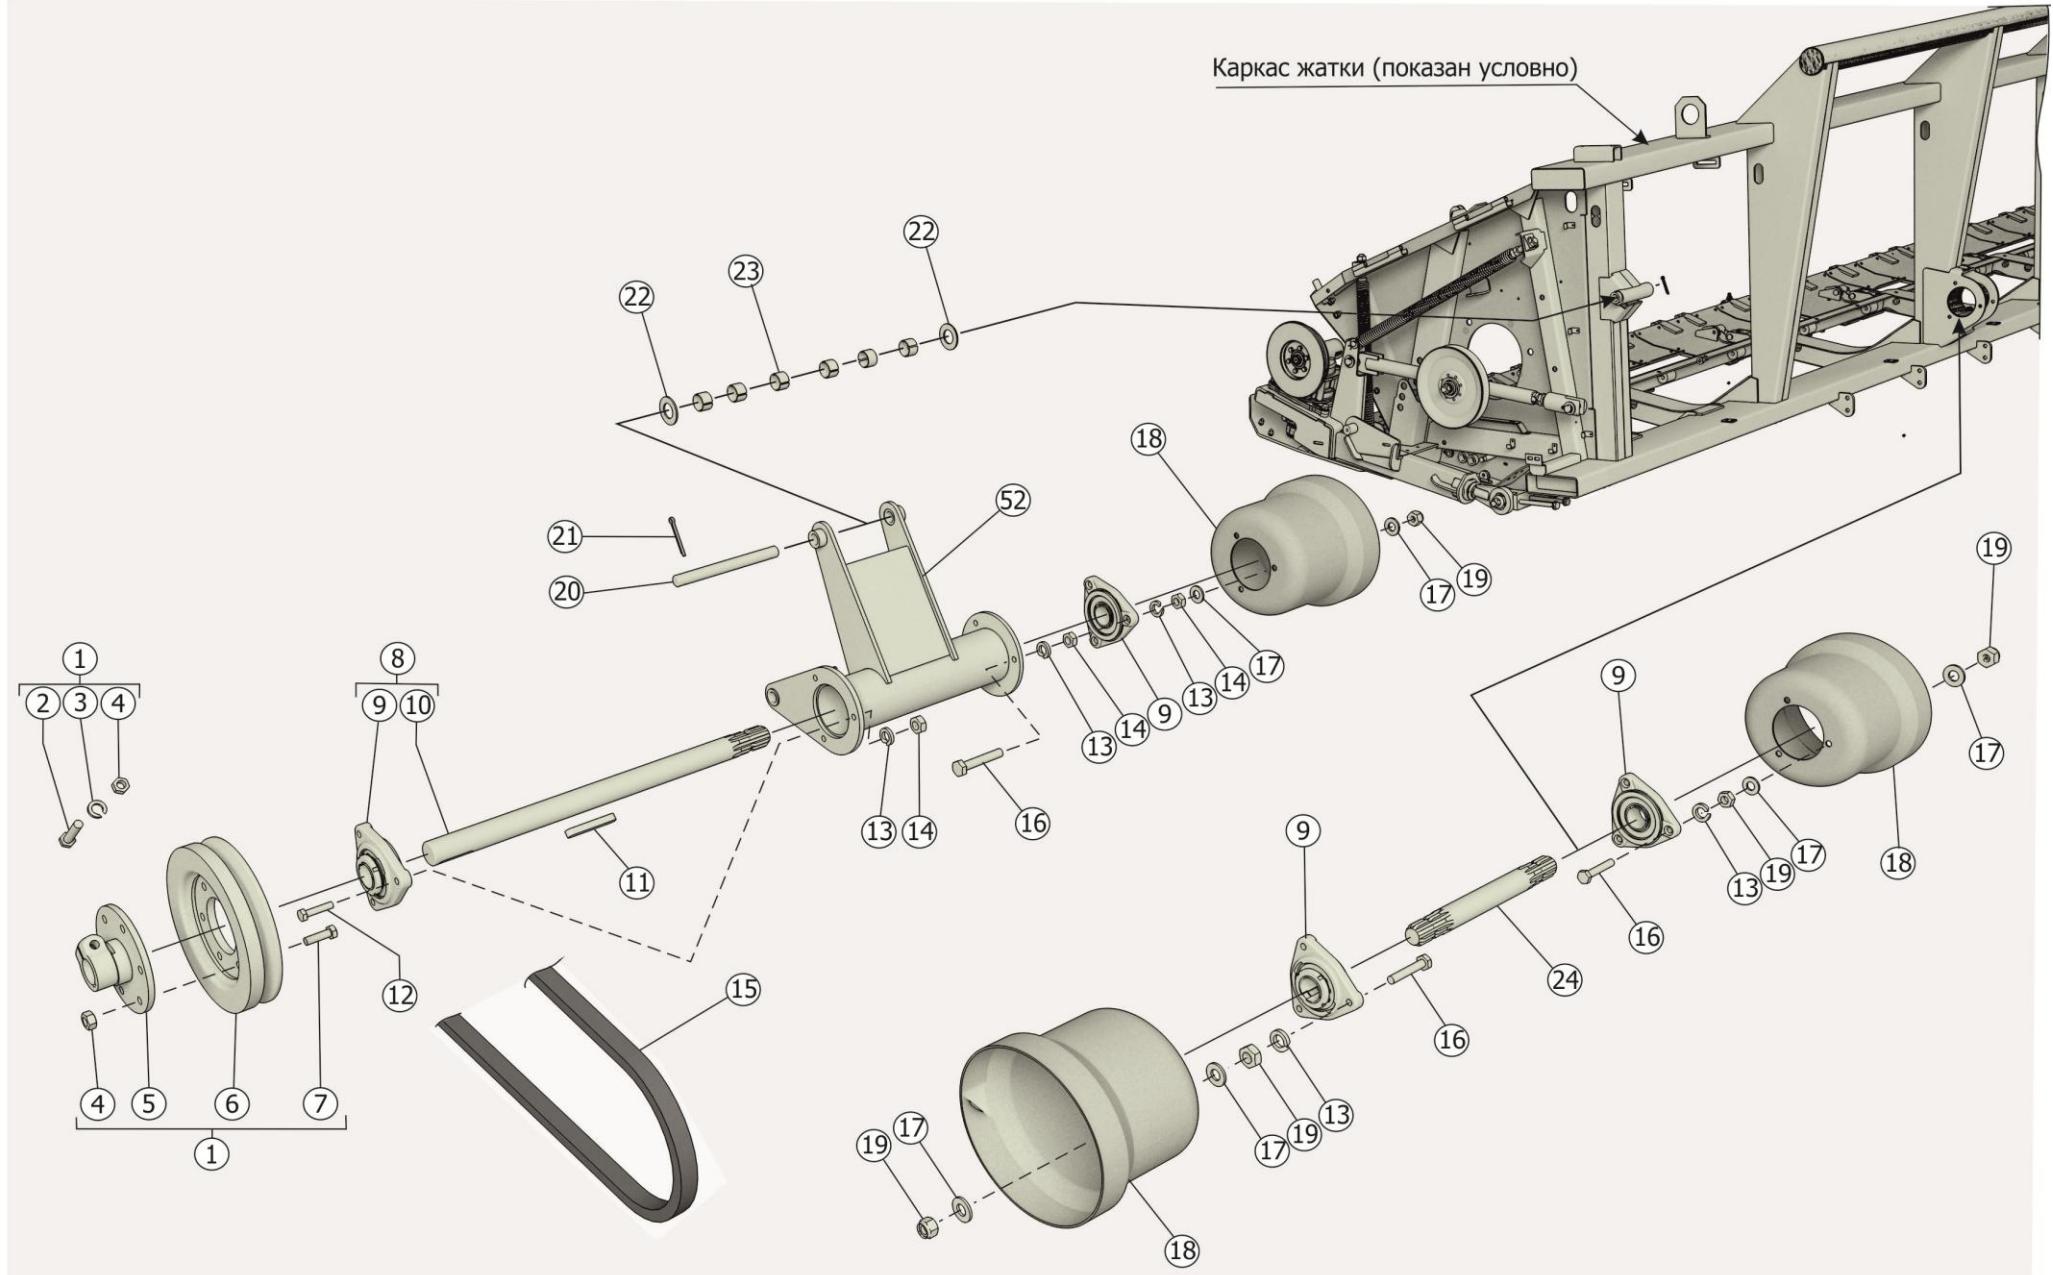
Привод режущего аппарата ЖСУ-901.01.03.500
